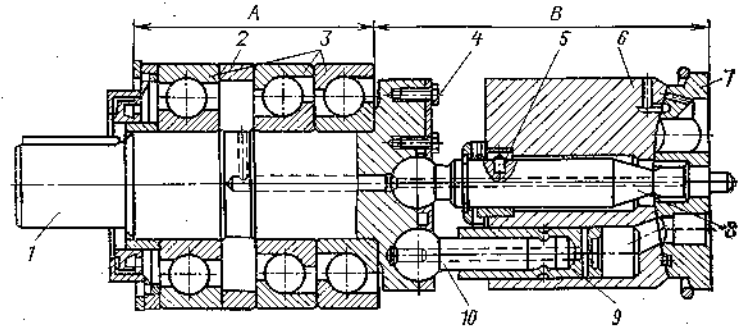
Унифицированный качающий узел аксиально-поршневых насосов: 1 — вал; 2 — распорная втулка; 3 — подшипник; 4 — прижимная пластина; 5 — штифт; 6 — блок цилиндров; 7 — распределитель; 8 — центральный шип; 9 — поршень; 10 — шатун; A и B — контрольные длины подшипникового и качающего узлов
